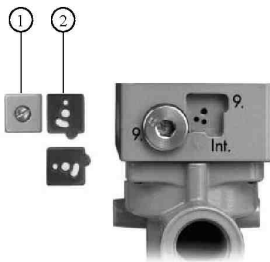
■ Реверсивное уплотнение, бустерный клапан
